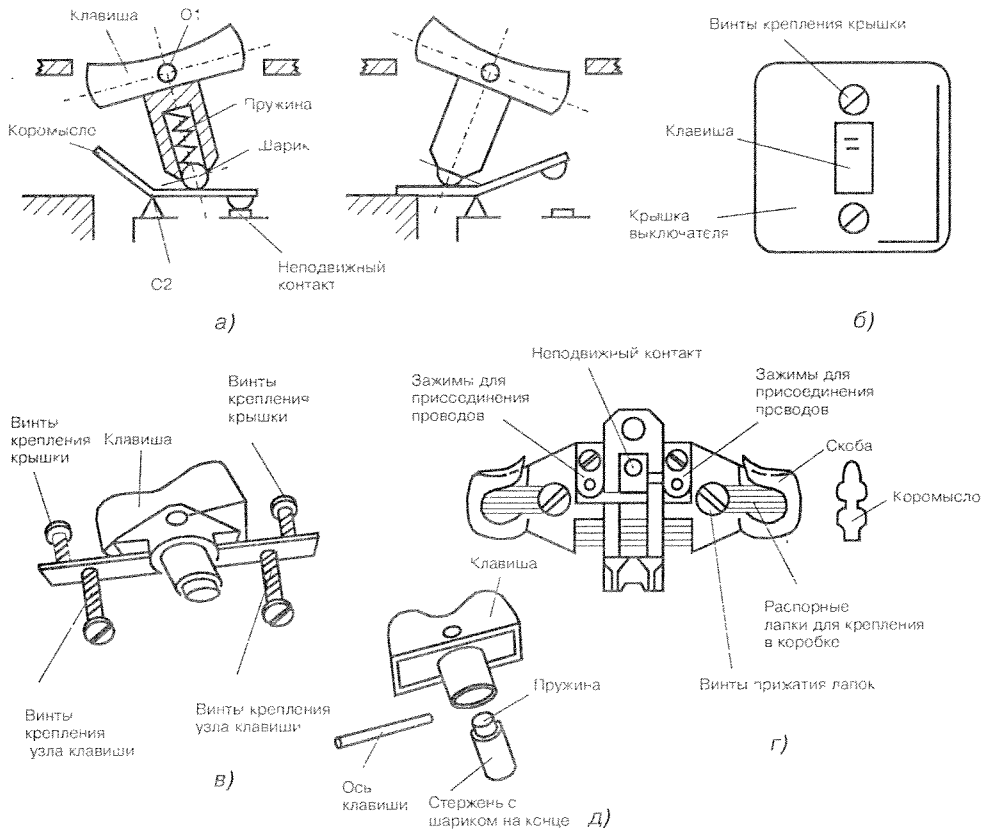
Принцип действия и устройство выключателя с клавишным приводом
